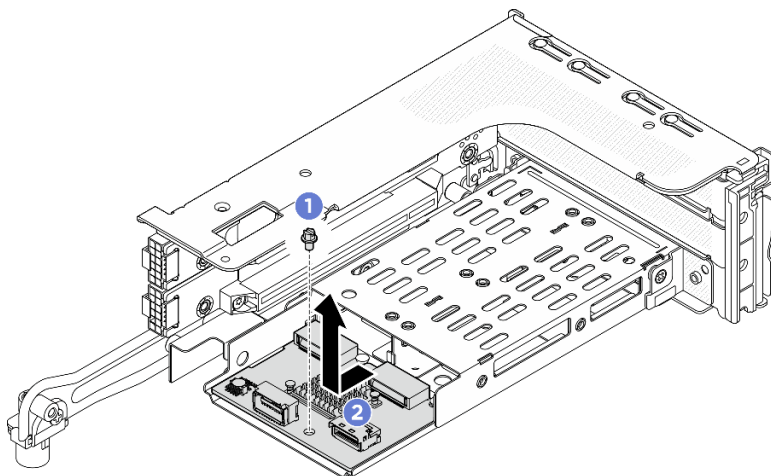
Entfernen der M.2-Rückwandplatine vom 3FH-M.2-Adapterrahmen
